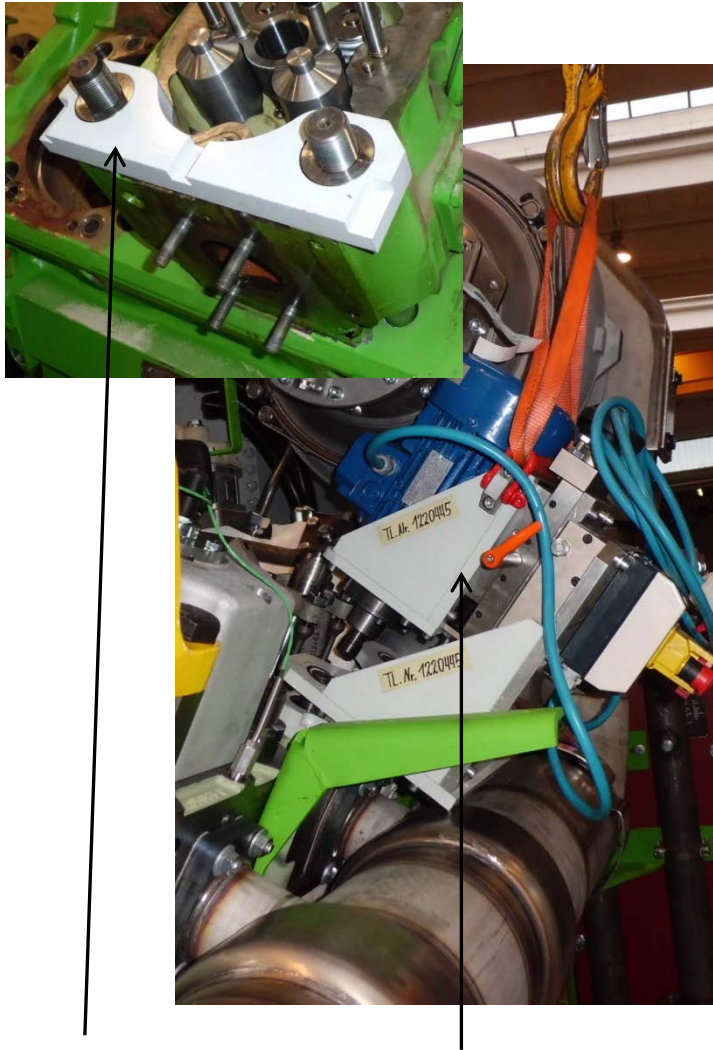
Unterlage montieren und die Fräsmaschine mit Hilfe eines Krans auf den Zylinderkopf heben
